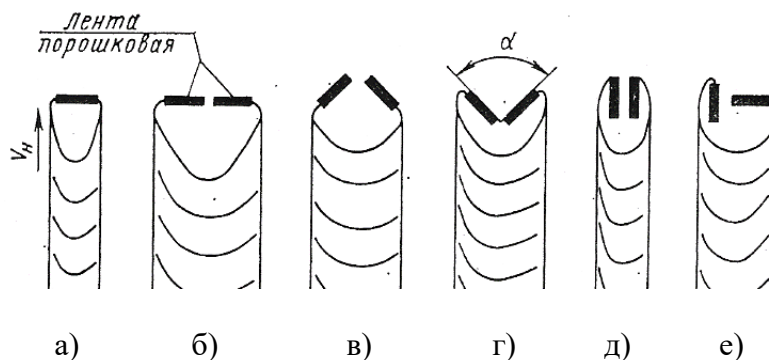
Схеми розташування порошкових стрічок при наплавленні
